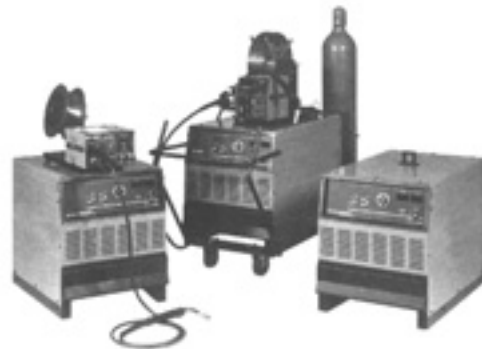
Exemples de postes de soudage GMAW
